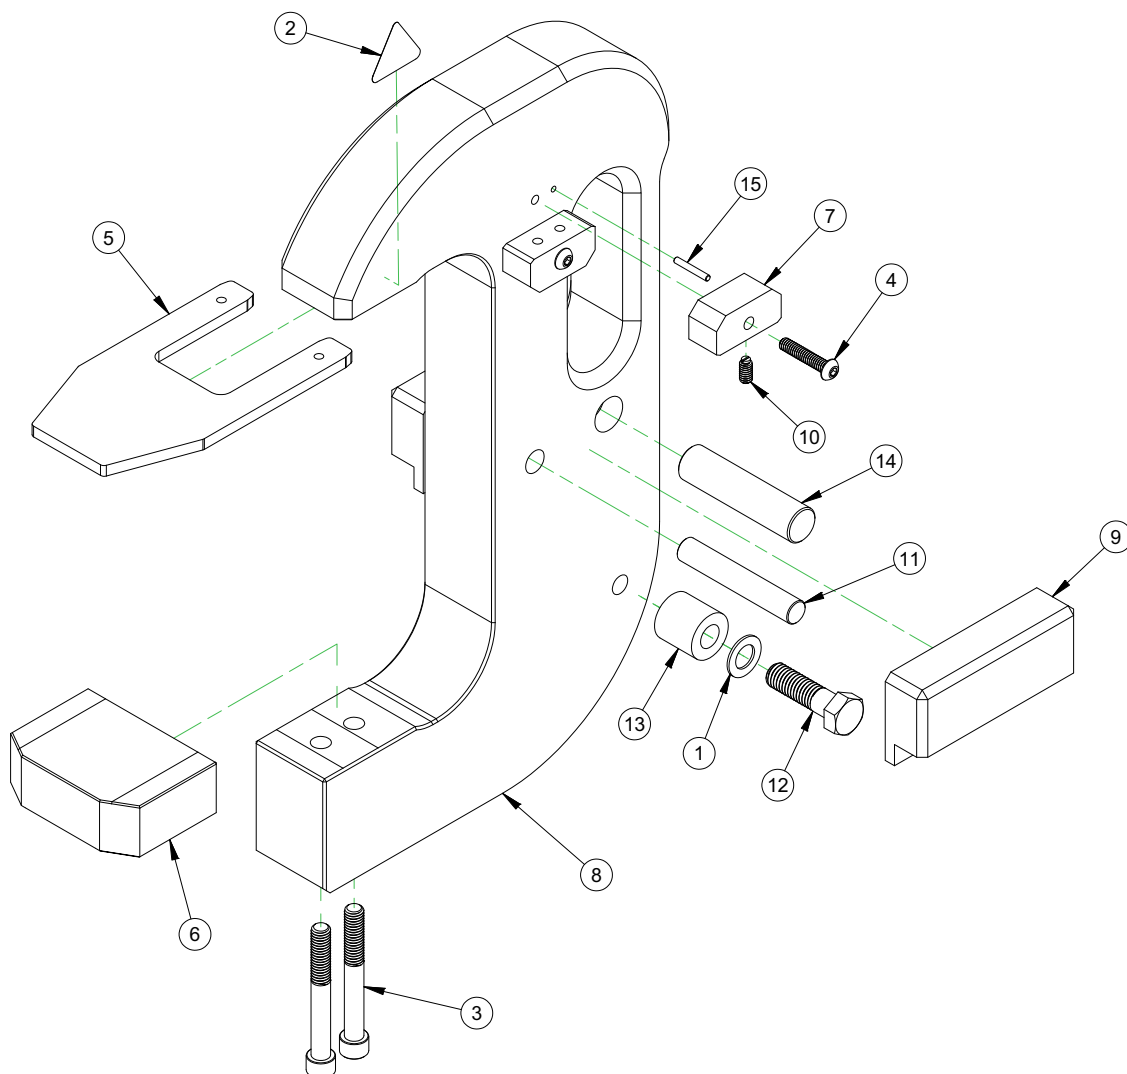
ENSEMBLE CONSOLE ÉTIQUETTES FACE ARRIÈRE (P/N 89417)
